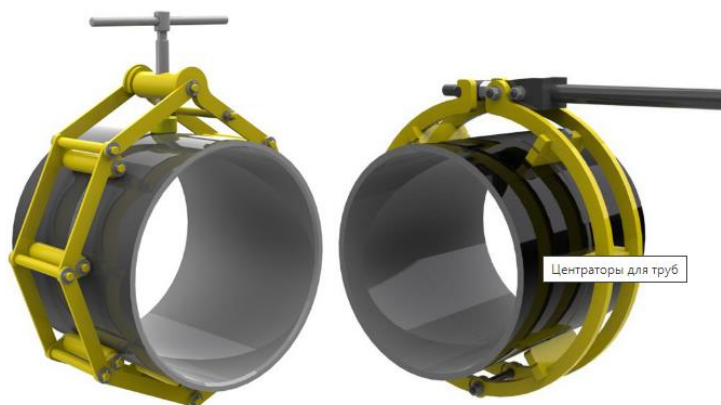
Центраторы для сварки труб ЦЗН
